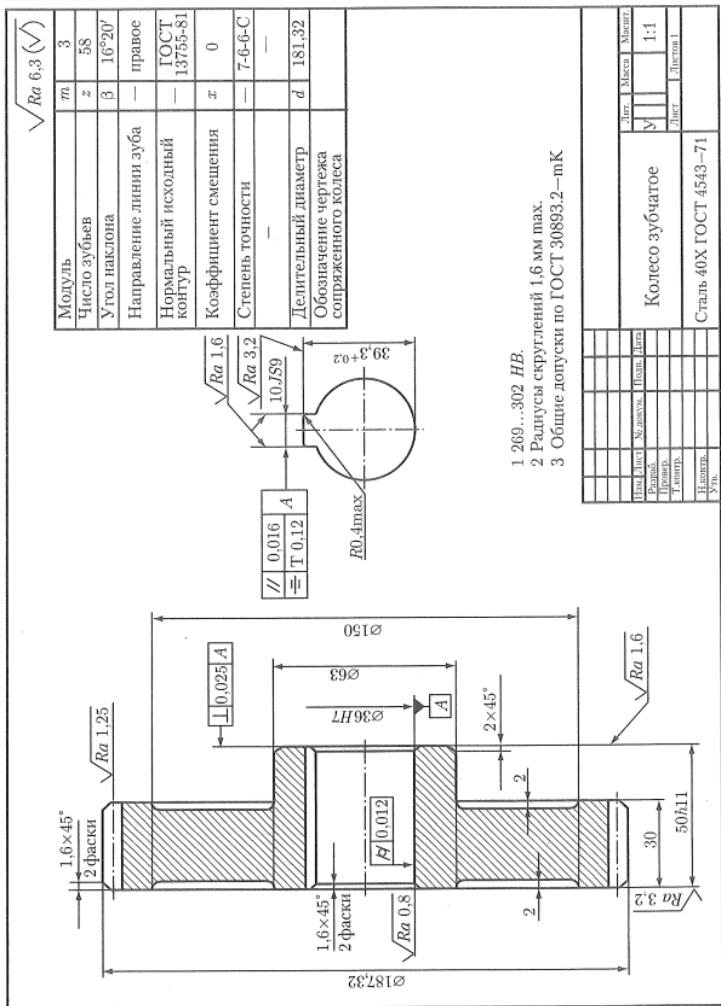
Рабочий чертёж цилиндрического зубчатого колеса
